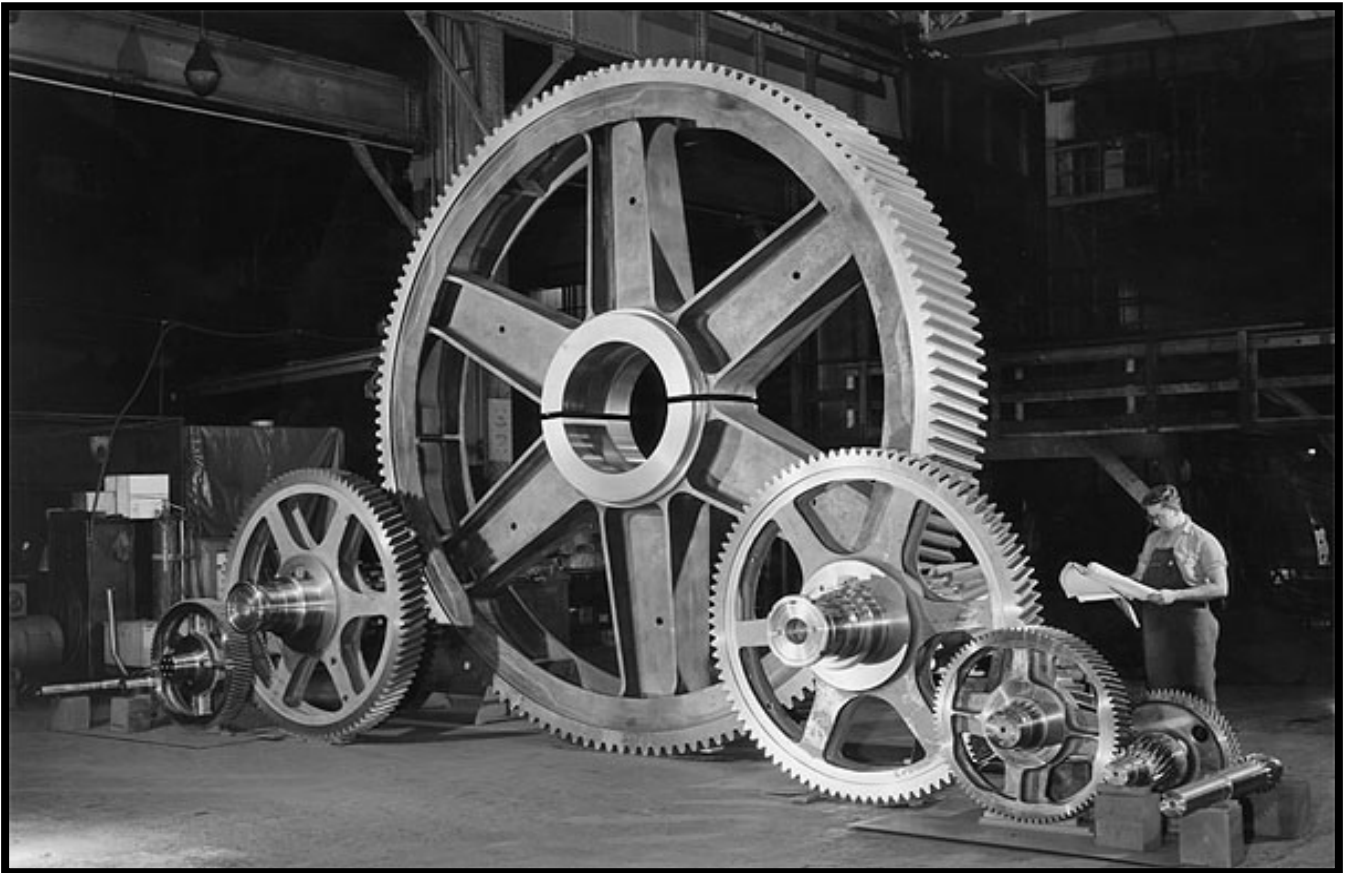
Engranajes de diversos tamaños fabricados para la planta de acero perteneciente a la “Pittsburgh Steel Co. at Monessen” en 1963. (Fuente: Foto de archivo de la empresa)
